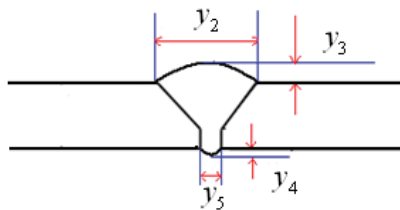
Parámetros geométricos del cordón de soldadura
